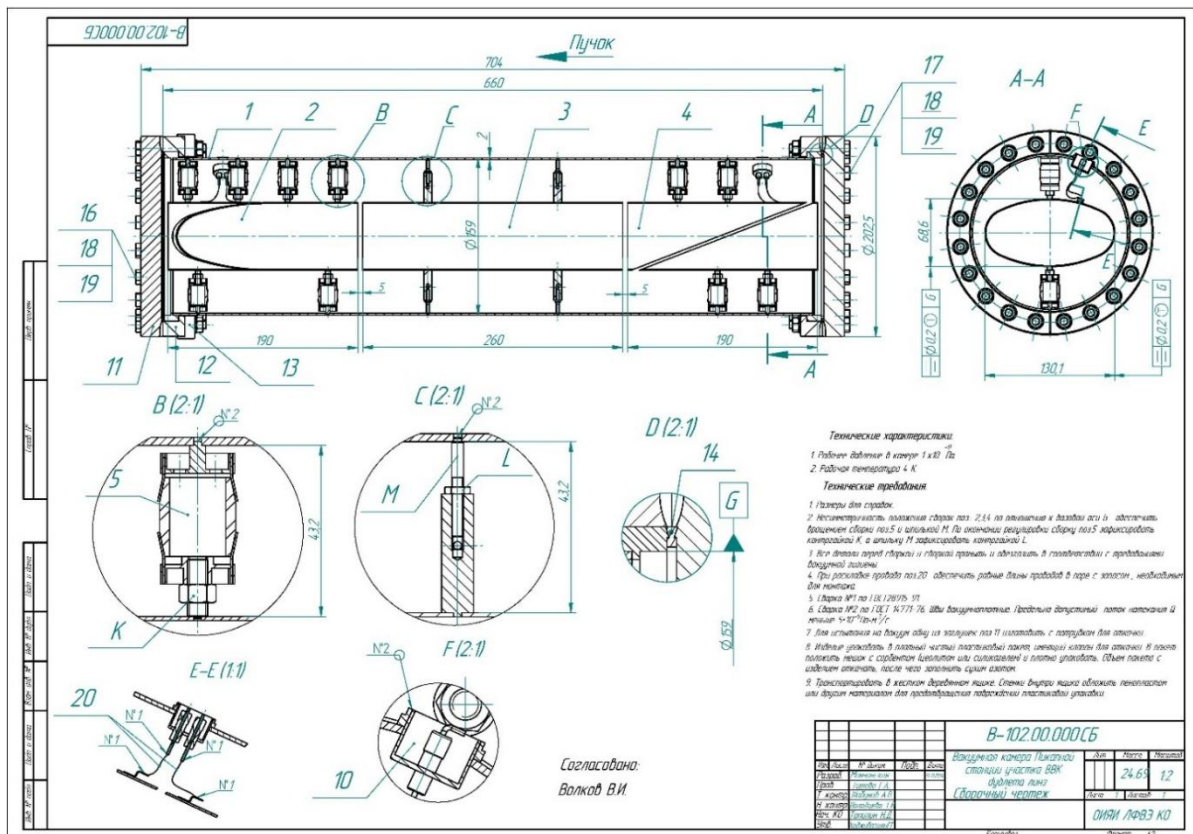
Сборочный чертёж пикап-электродов блока линз
